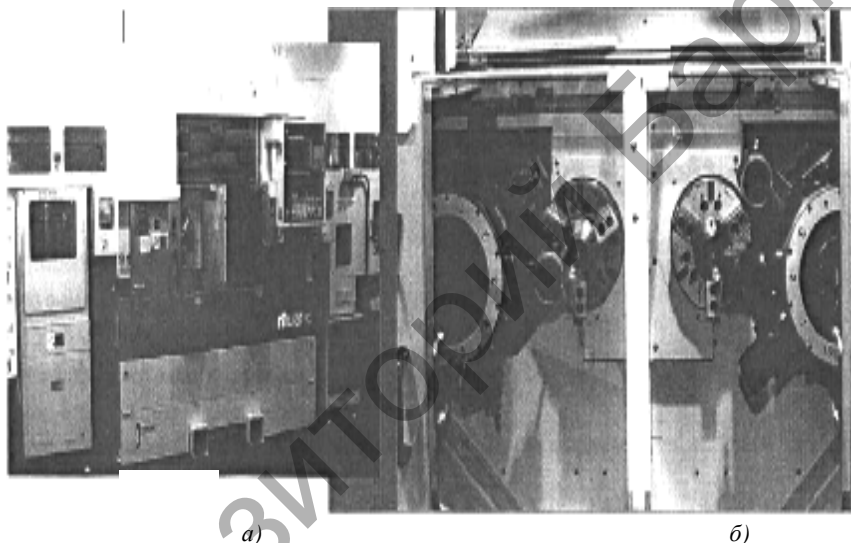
Общий вид (а) и шпиндельный узел (б) токарного двухшпиндельного станка фирмы Murata (Япония)
